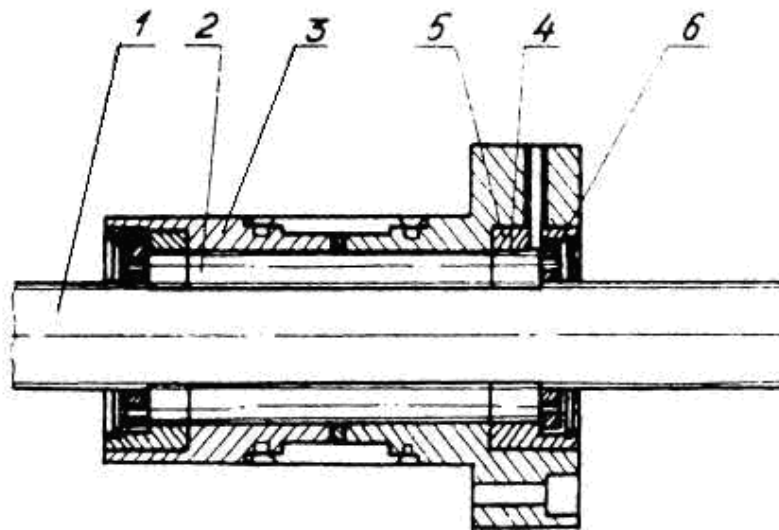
Передача винт-гайка с короткими резьбовыми роликами и двумя гайками с выборкой зазора
